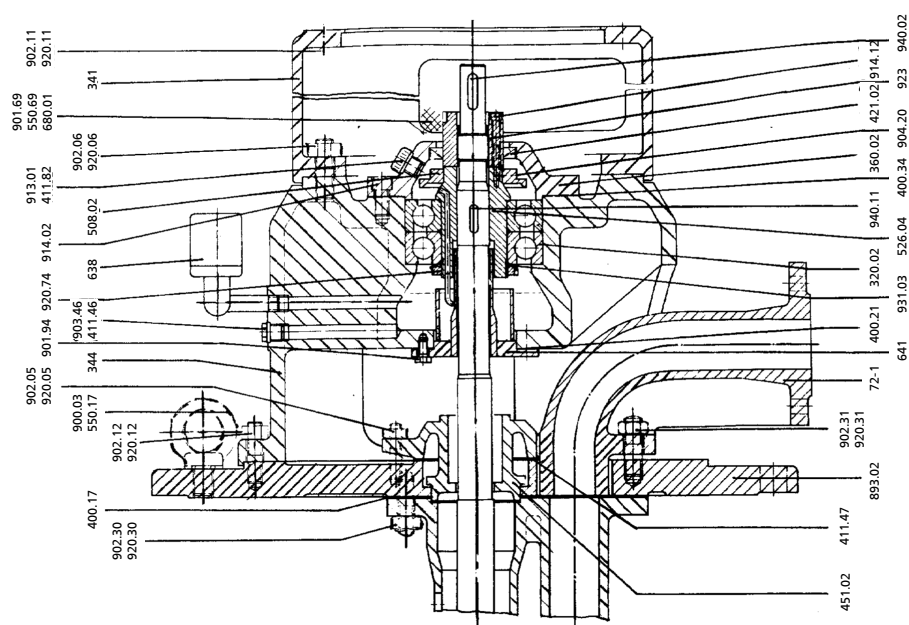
Расположение деталей насоса с габаритами 80/100/125/150/200/250
